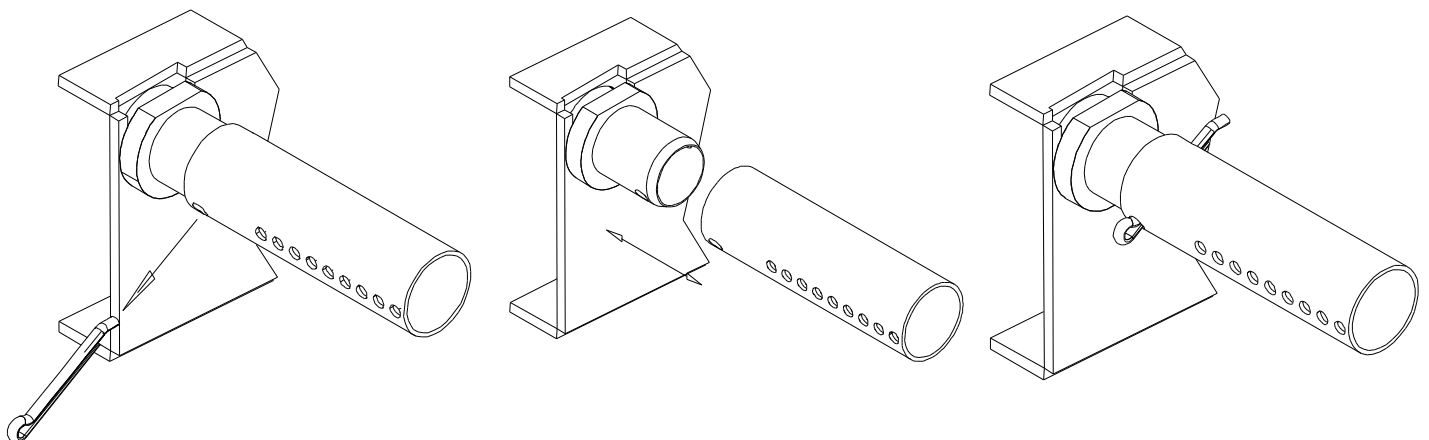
Remplacement des tubes d'aération auxiliaires
